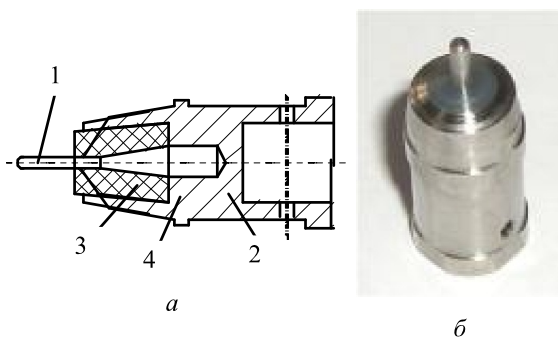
Конструкція клапана із конічною гумовою поверхнею золотника: а конструктивна схема золотника; б — загальний вигляд золотника
